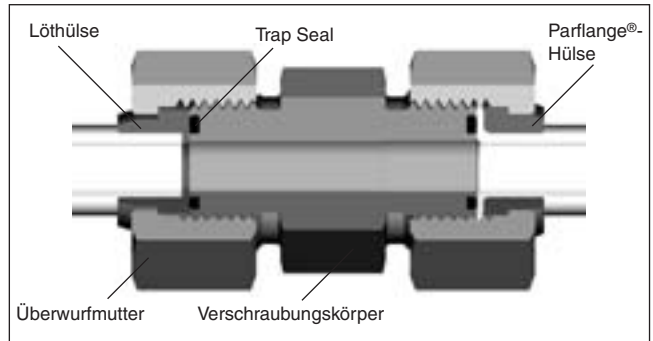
Ausschnitt einer O-Lok®-Verbindung mit Flansch- und Lötverschraubungen.
